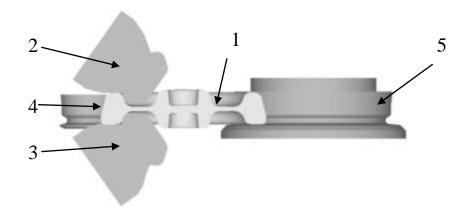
начальный момент осадки обода по ширине наклонными валками: 1 — заготовка колеса перед прокаткой, 2 — верхний наклонный валок, 3 — нижний наклонный валок, 4 — нажимной валок, 5 — коренной валок.
